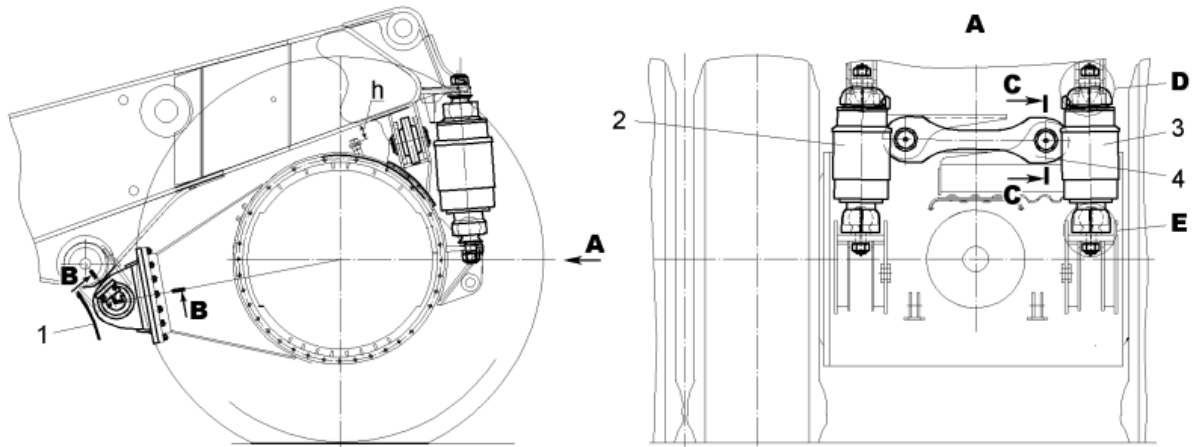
Задняя подвеска автосамосвала БЕЛАЗ-7513. 1 – штанга; 2, 3 – пневмогидравлический цилиндр; 4 – штанга подвески [56]
